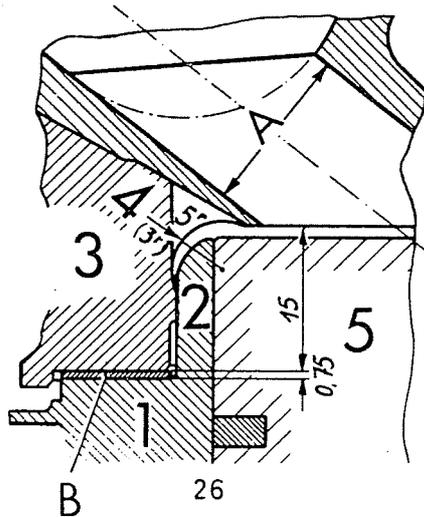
Merkmale von Zylinder und Zylinderkopf früherer Ausführungen (Maßangaben in mm)
